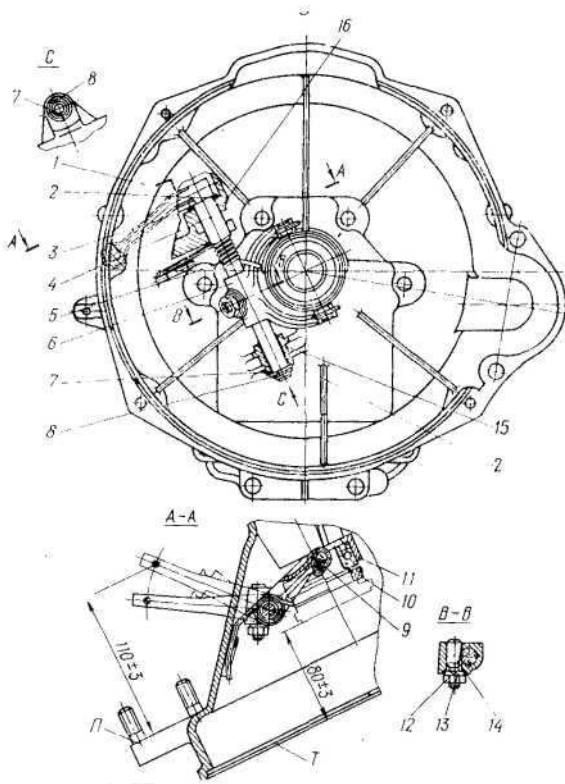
Механизм выключения сцепления: 1 — картер сцепления; 2, 3 — нижняя и верхняя втулки оси; 4 — ось вилки с рычагом в сборе; 5 — возвратная пружина вилки выключения; 6 — вилка выключения; 7 — шайба регулировочная; 8 — пружинное кольцо; 9 — звено соединительное; 10 — подпятник; 11 — обойма подпятника; 12 — гайка; 13 — шайба пружинная; 14 — клин крепления вилки выключения сцепления фиксирующий; 15, 16 — нижний и верхний приливы
